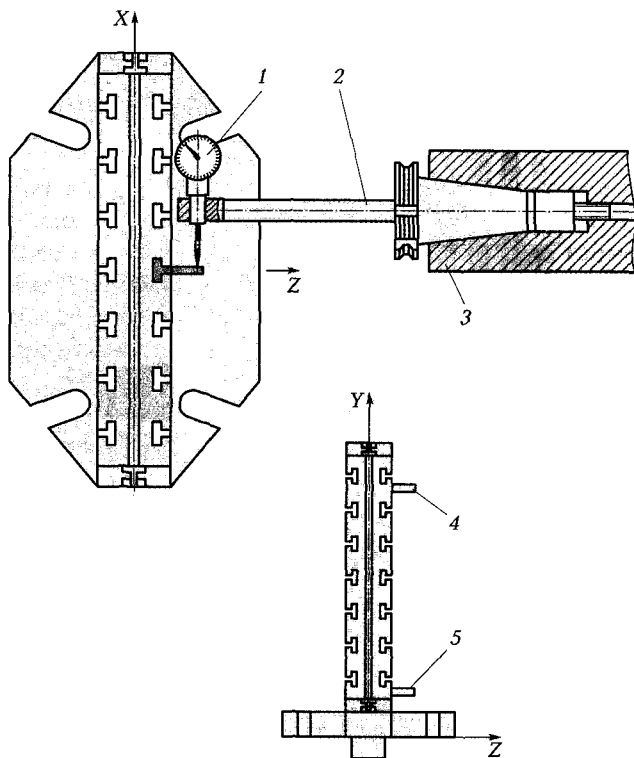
Точки измерения положения приспособления в направлении оси Y :
